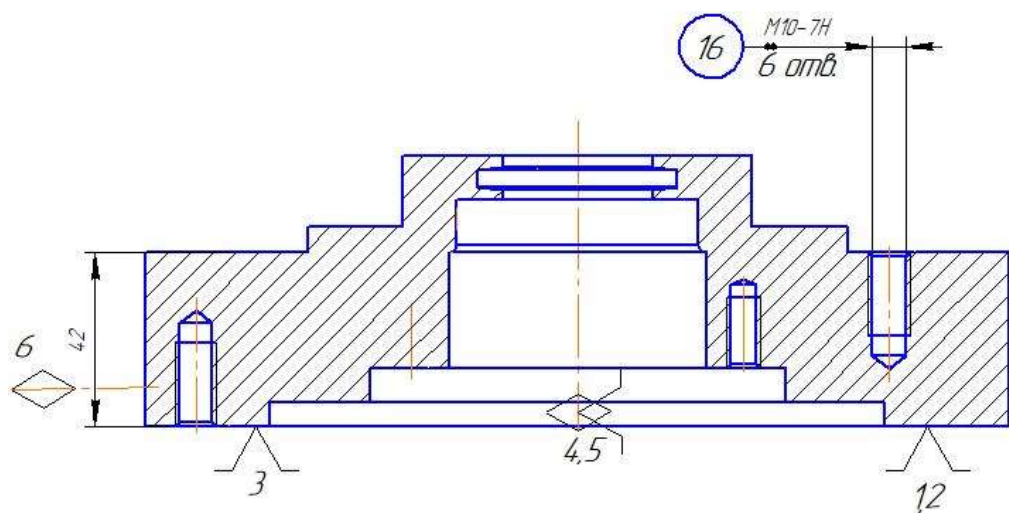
Ескіз механічної обробки із схемою базування (операція 020)
